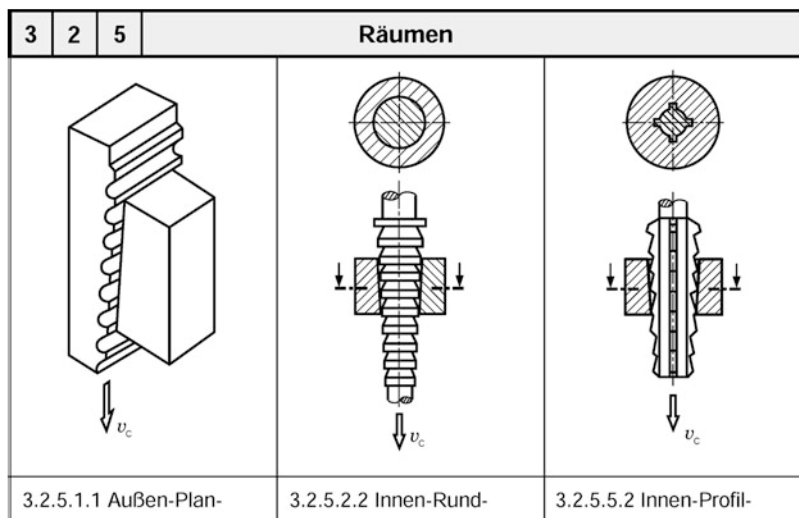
Plan-, Rund- und Profilräumverfahren / Procedee de broșare plană, cilindrică, profilată [WES 10]
